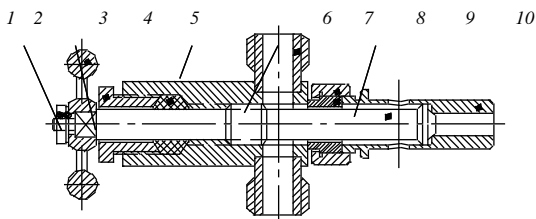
Приспособление КИ-6272: 1 – гайка; 2 – шайба; 3 – маховичок; 4 – гайка нажимная; 5 – набивка; 6 – штуцер; 7 – гайка накидная; 8 – ниппель; 9 – игла запорная; 10 – штуцер переходной
